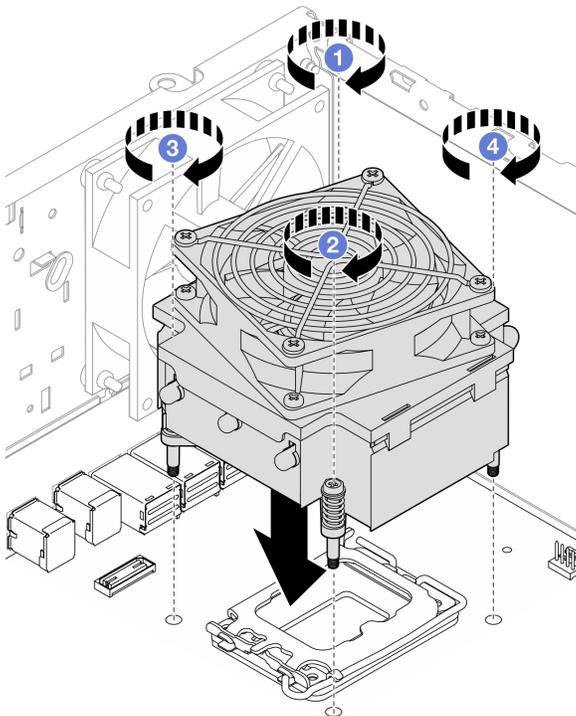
Serrage des vis du module dissipateur thermique et ventilateur pour les processeurs avec une enveloppe thermique inférieure à 95 W
